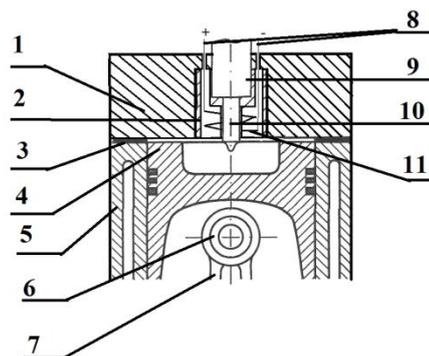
Схема нанокерамической вставки головки блока цилиндров с электронагревательным элементом: 1- головка блока цилиндров, 2- нанокерамическая вставка, 3- прокладка головки блока цилиндров, 4- поршень, 5- блок цилиндров, 6- палец шатуна, 7- шатун, 8- полюсные выводы, 9- корпус распылителя форсунки, 10 – распылитель форсунки, 11- электронагревательного элемента.
